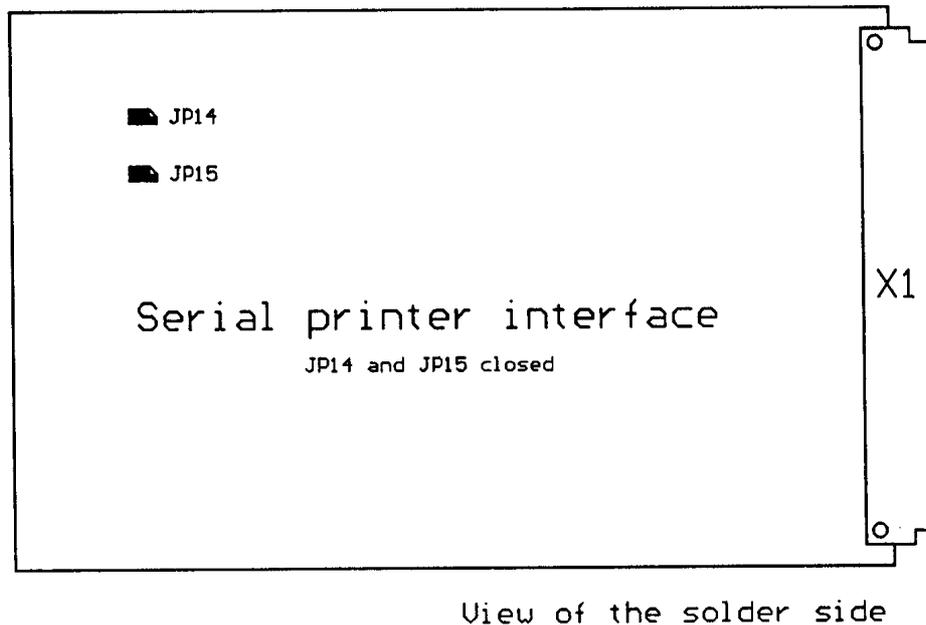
Jumperpositionen und Jumperbestückung für die Druckerschnittstelle
